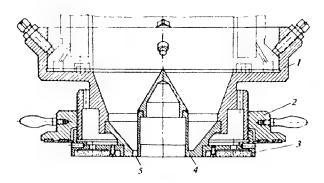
Приставка пескострельной машины модели 28Б5: 1 корпус; 2 регулировочная тайка; 3 вентиляционная плита; 4 корпус; 5 кольцевые дюзы
